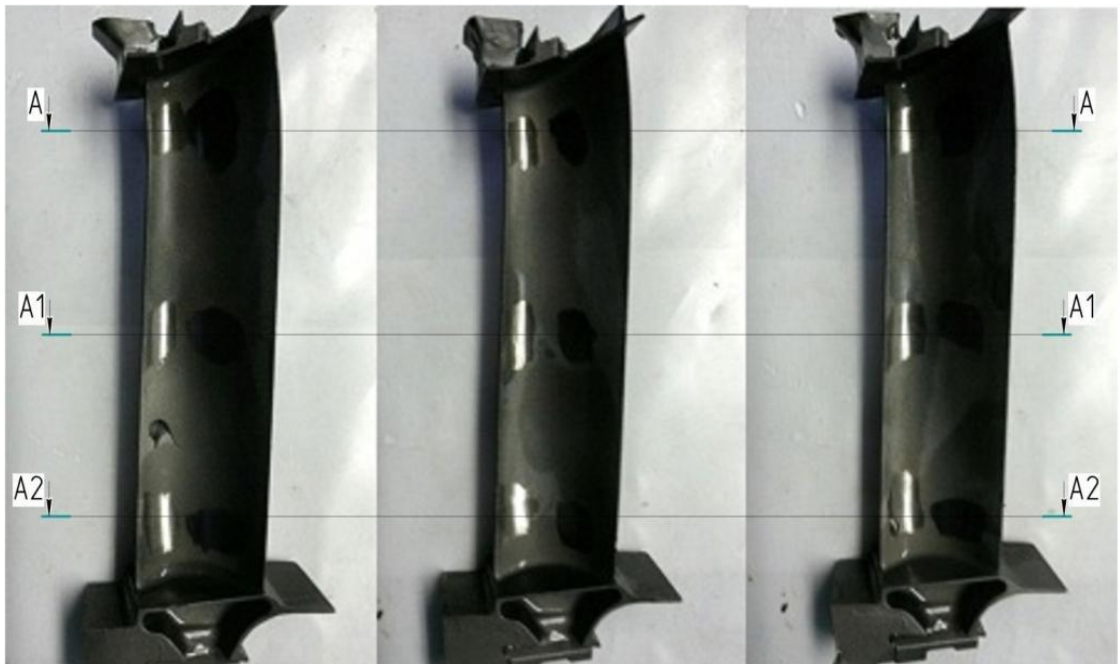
Розташування перерізів, за якими здійснювався контроль стінок лопатки
